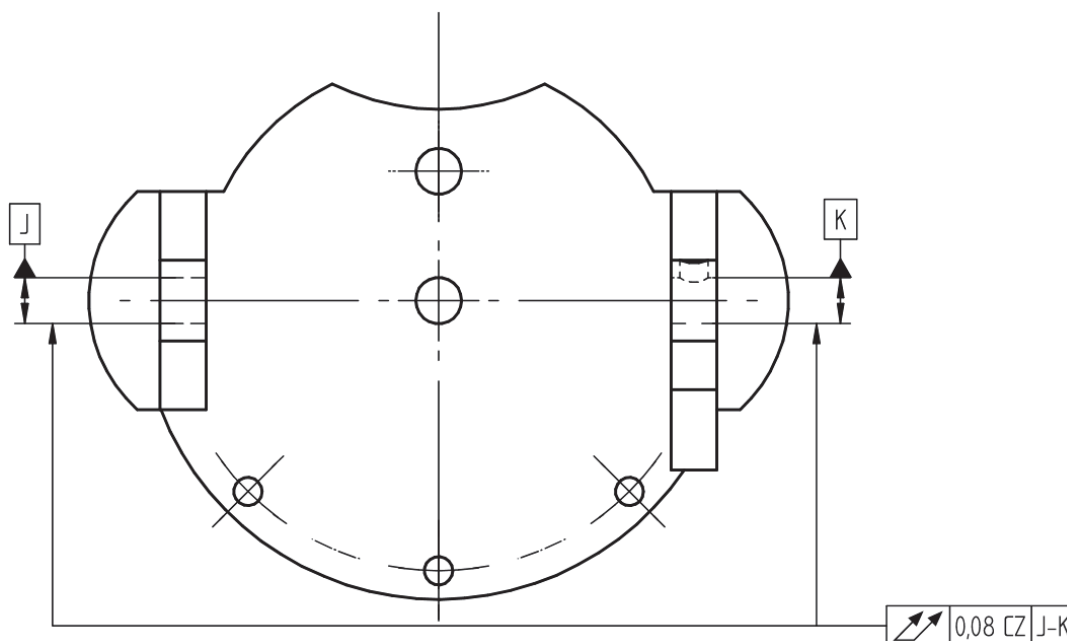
Nesouvisející tolerance pro součást "otočný stůl"
